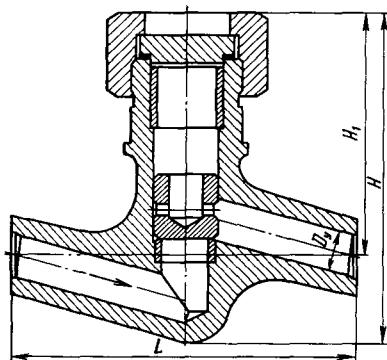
Клапан обратный подъемный типа 922 (3с-6-1)
